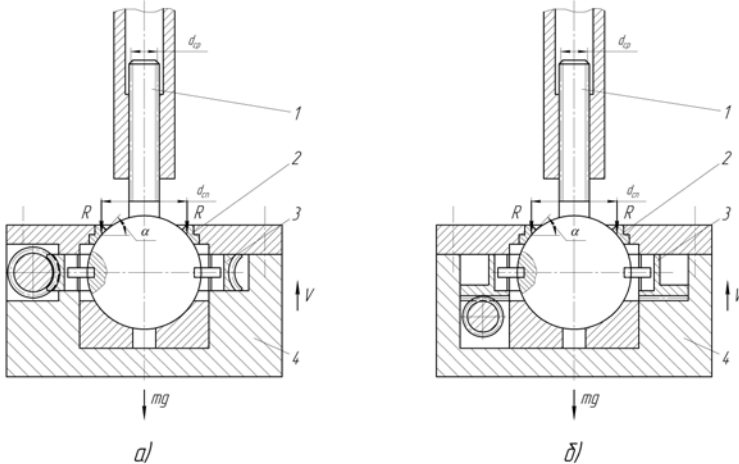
Схема к расчету исходных данных для проектирования редуктора механизма регулировки закрытой высоты однокривошипного пресса:
